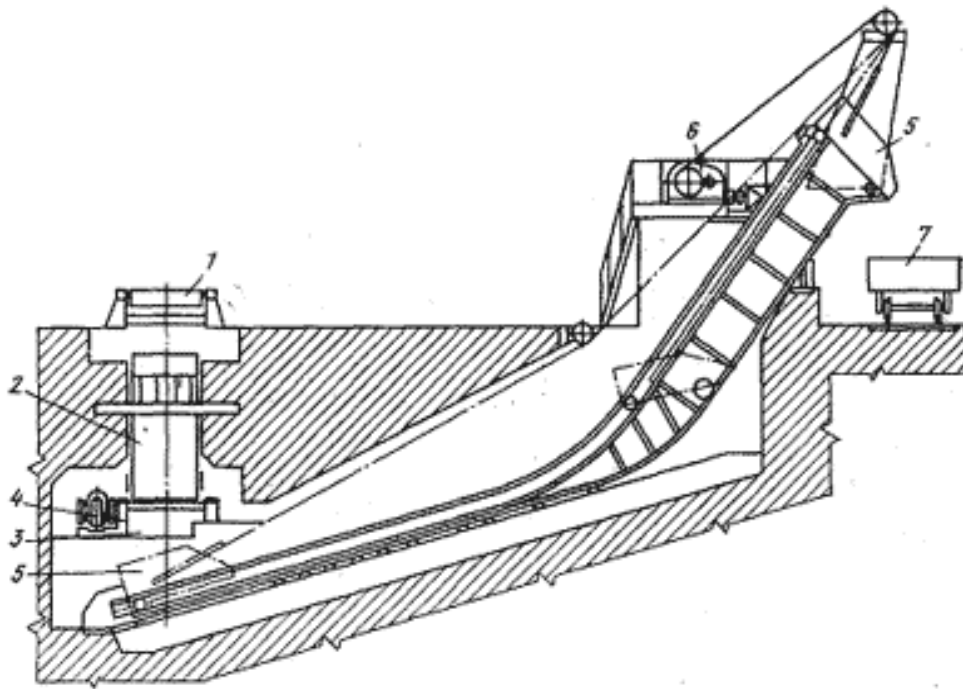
Скиповый подъемник для уборки окалины и кусков скрапа из-под рабочего рольганга
